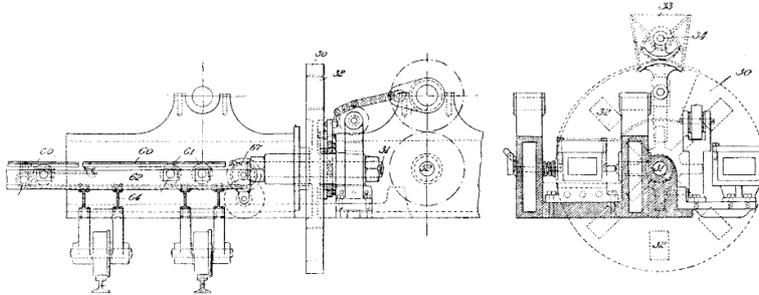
et 6. — Presse Wyssling. Coupe F D (fig. 3) et vue par bout.
